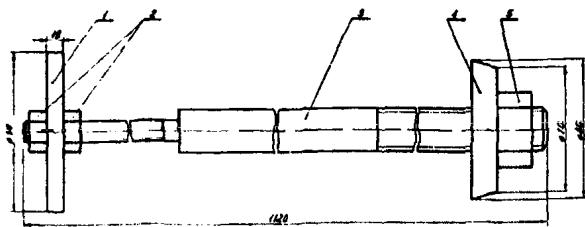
Приспособление для разборки и сборки механизмов камеры:
